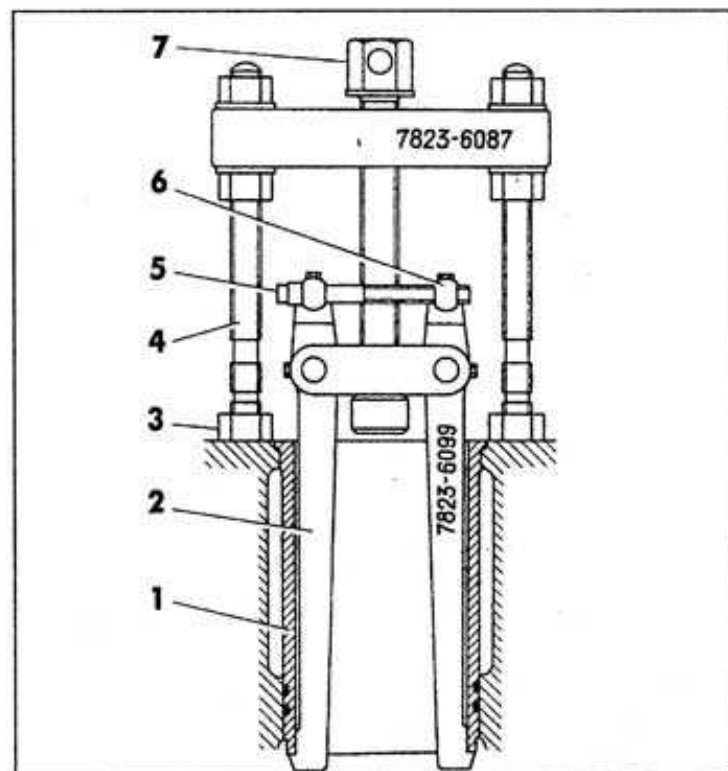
Выпрессовка гильзы из блока цилиндров комбинированным съемником:
